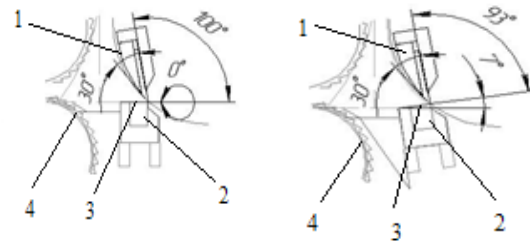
Схеми розташунок робочої поверхні контрножа в барабанній деревинорубальній машині: 1 – різальний ніж; 2 – контрніж; 3 – робоча поверхня контрножа; 4 – нижній зубчастий валець механізму подавання
